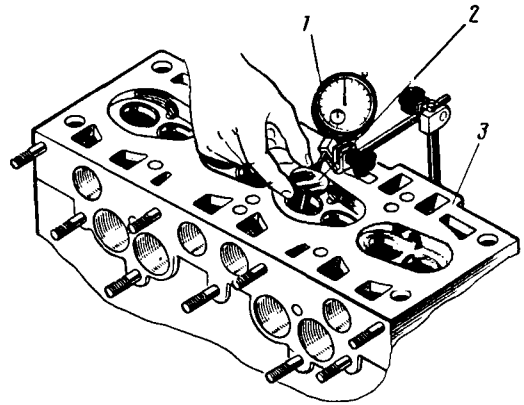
Проверка зазора между стержнем клапана и направляющей втулкой клапана:
